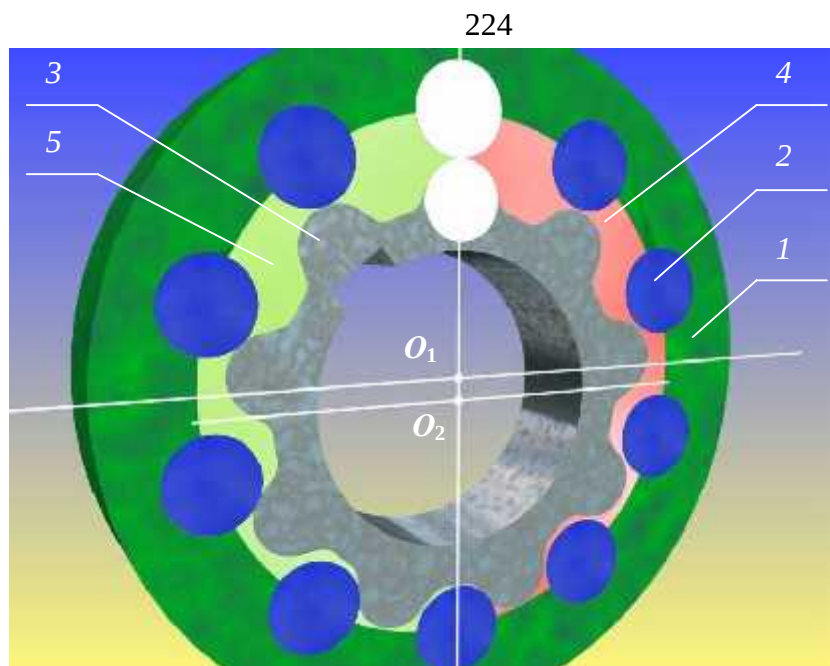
Героторное движение вытеснителей: 1 – охватывающий вытеснитель; 2 – ролики; 3 – охватываемый вытеснитель; 4 – зона нагнетания; 5 – зона слива.
